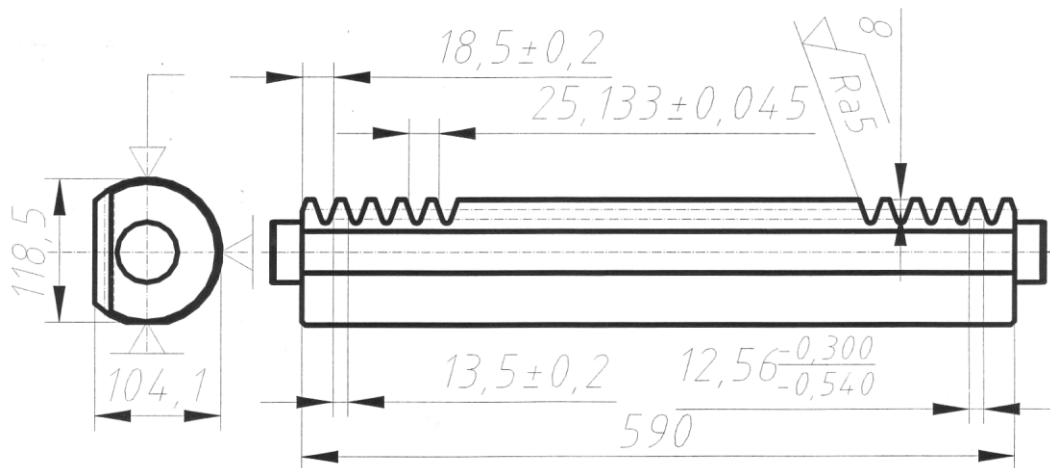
Ескіз обробки деталі операція №055
